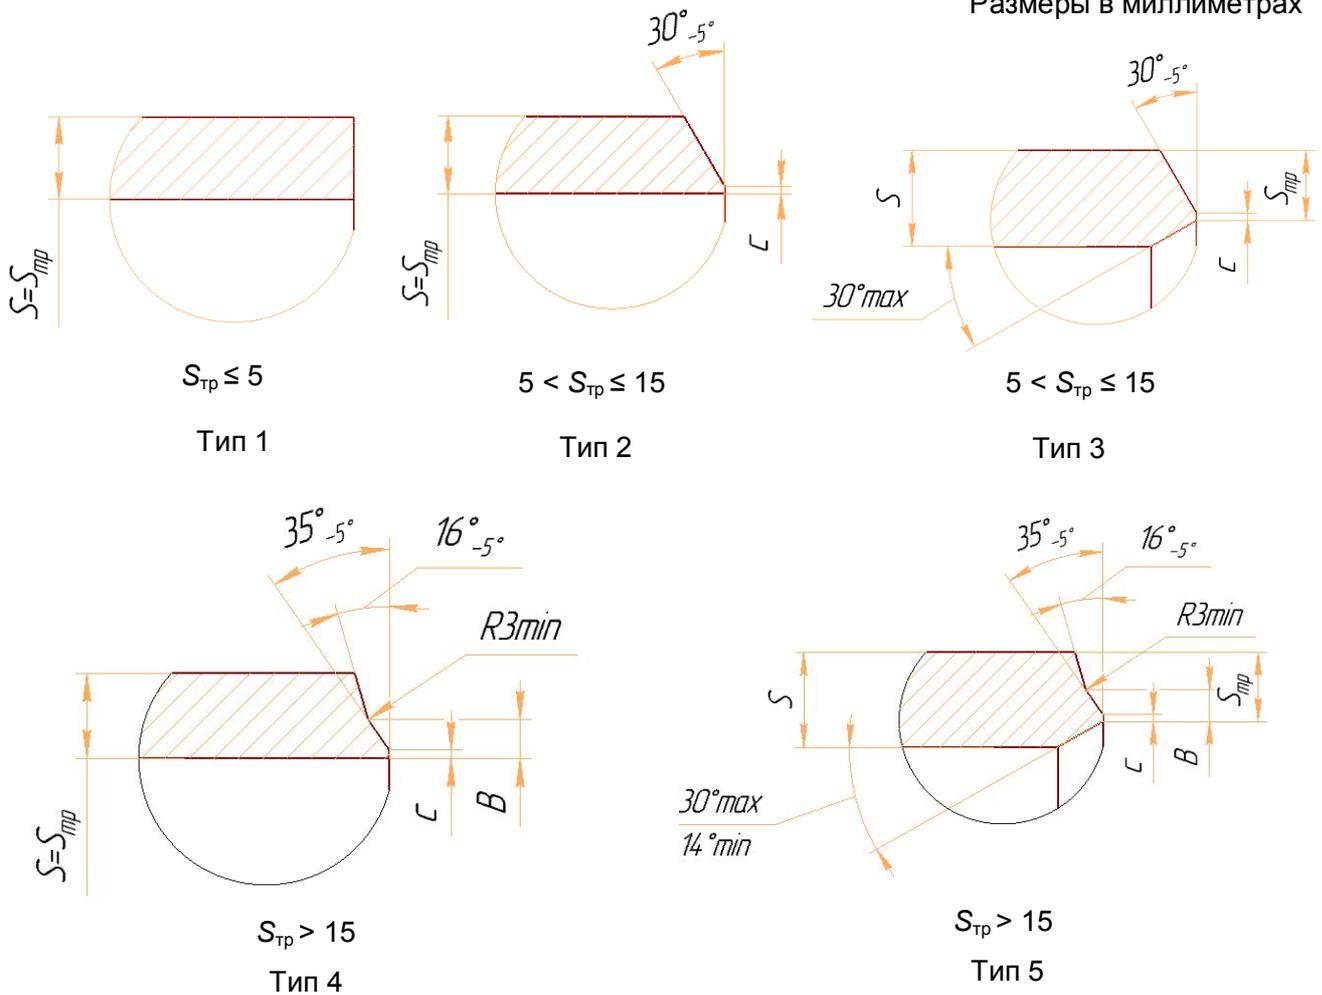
Типы обработки кромок торцов отводов под сварку
